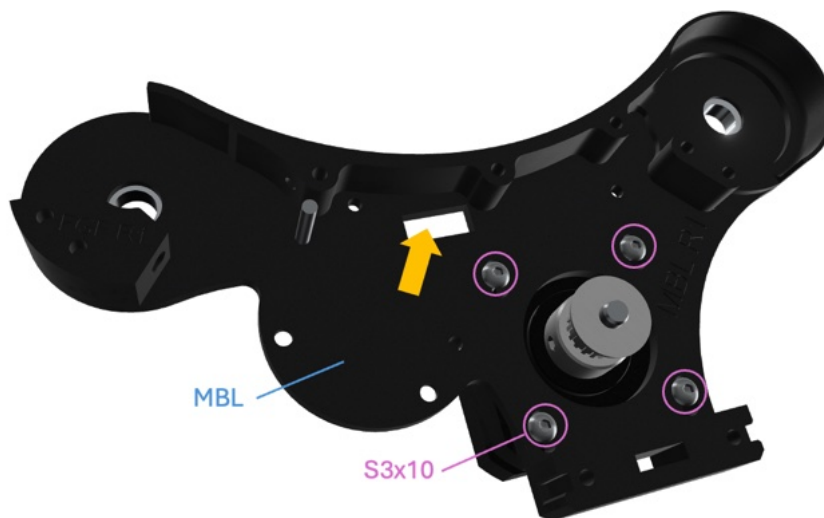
Rewinder-Chassis Montageschritt 6.
